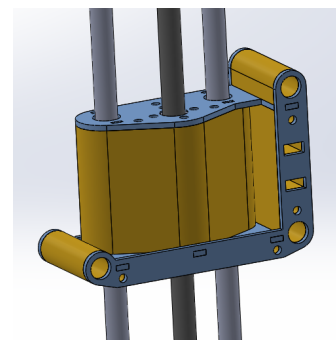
Carro Z con guías y varilla trapezoidal
